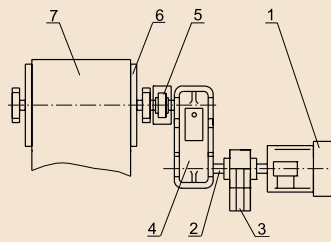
Привод ленточного конвейера на базе цилиндрического редуктора:
